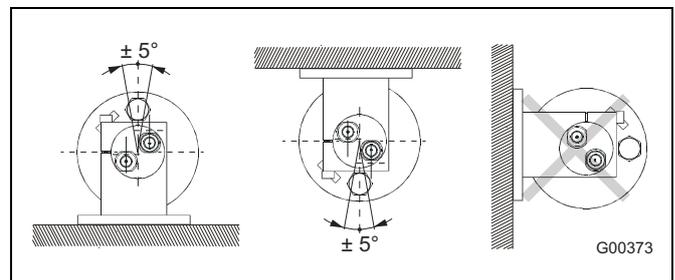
Ángulo de giro – conector múltiple – posición horizontal
